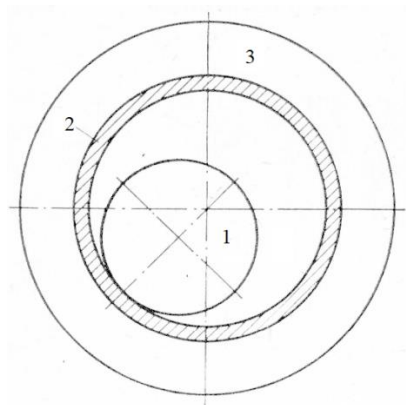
3. Схема неметаллического подшипника скольжения с полным углом охвата. 1 — жесткий вал, 2 — упругий кольцевой слой (вкладыш), 3 — жесткая обойма.
